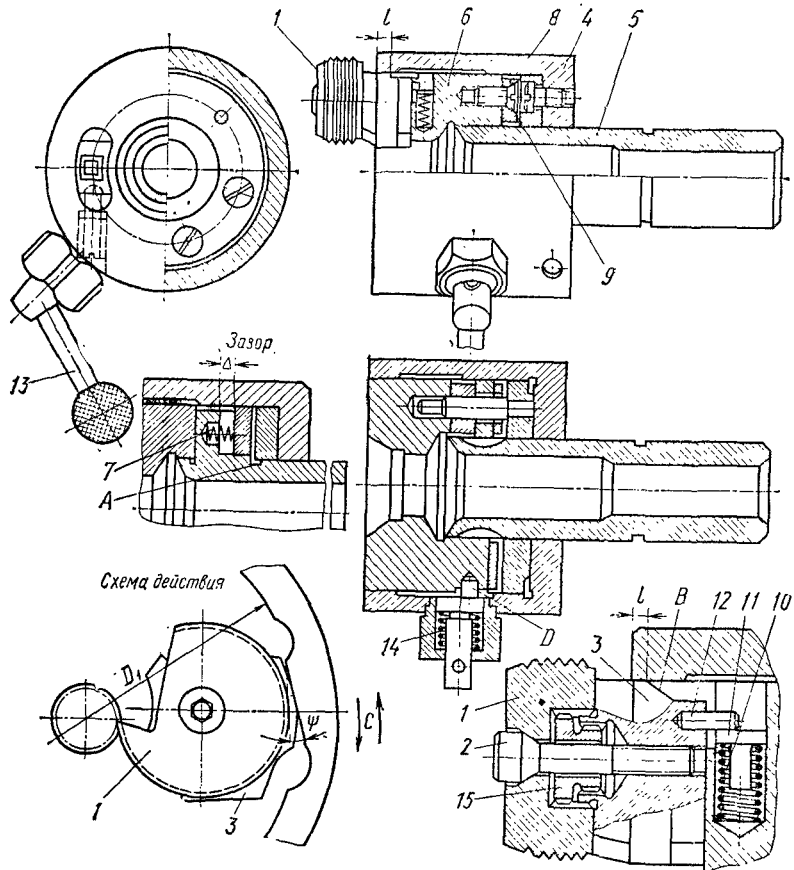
Резьбонарезная неврращающаяся головка с круглыми гребенками
